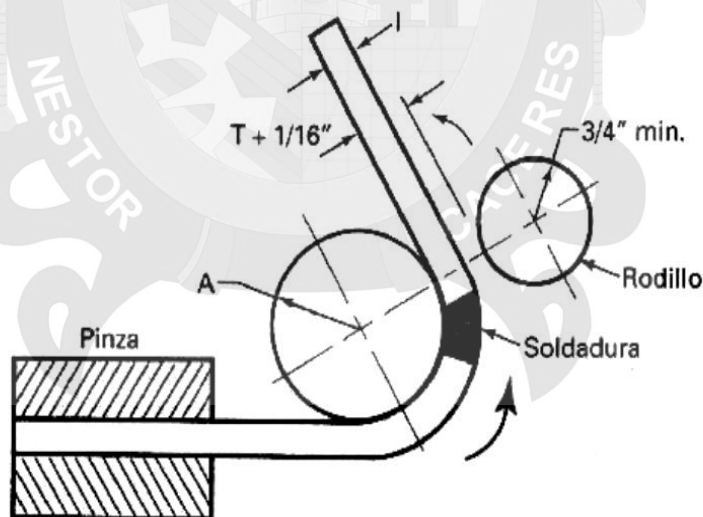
Las pruebas mecánicas de soldadura incluyen flexión guiada de las soldaduras de garganta.
